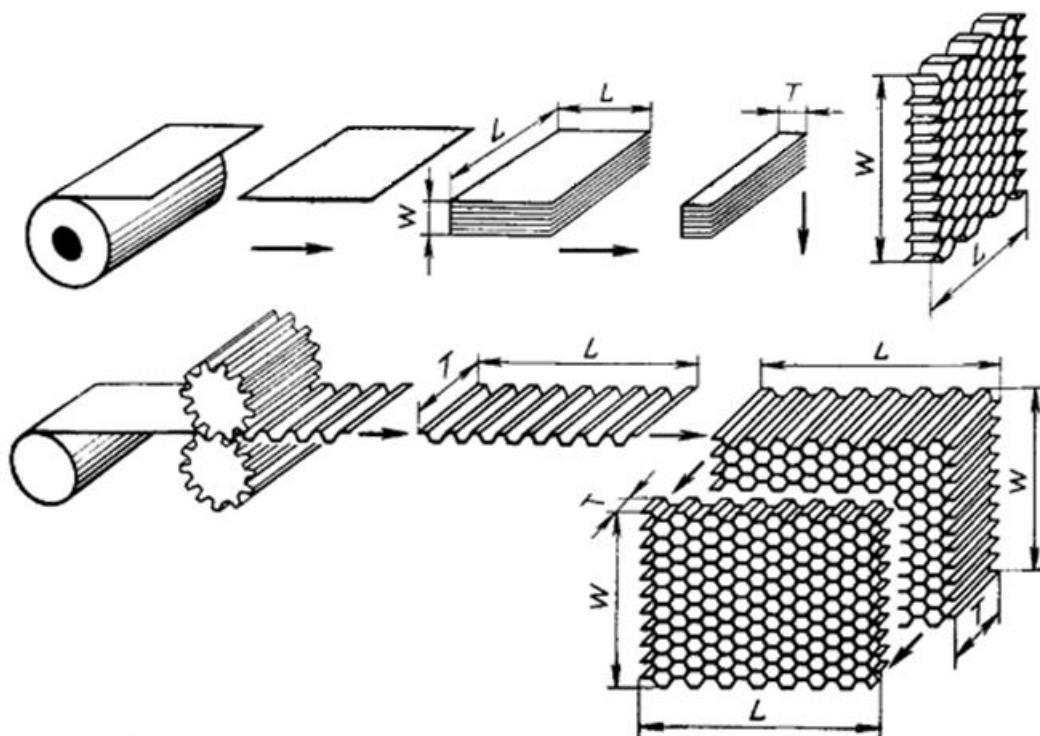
Схема виготовлення сотового заповнювача
